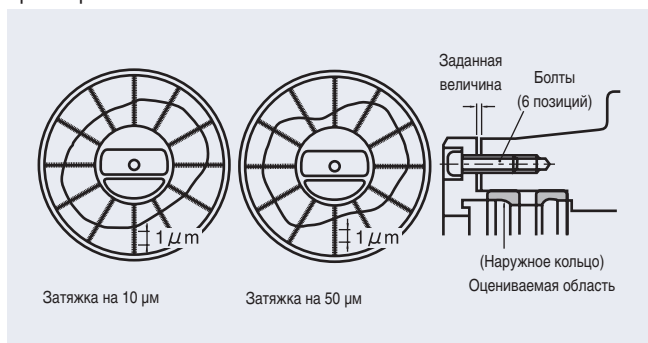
Деформация наружного кольца двухрядного цилиндрического роликового подшипника, вызванная чрезмерной затяжкой.
